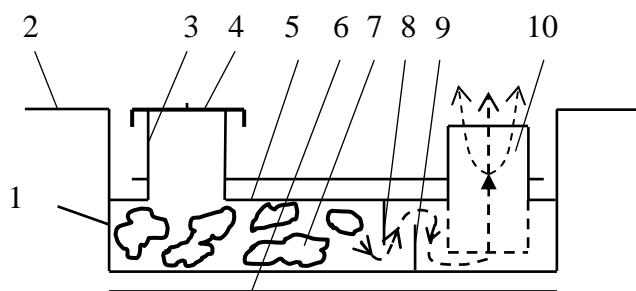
Испаритель косвенного нагрева лабиринтного типа: 1 – коробочка; 2 – лапки; 3, 4 – патрубок для загрузки материала и его крышка; 5 – крышка испарителя; 6 – нижний экран; 7 – испаряемое вещество; 8, 9 – разделительные экраны; 10 – выходной патрубок
